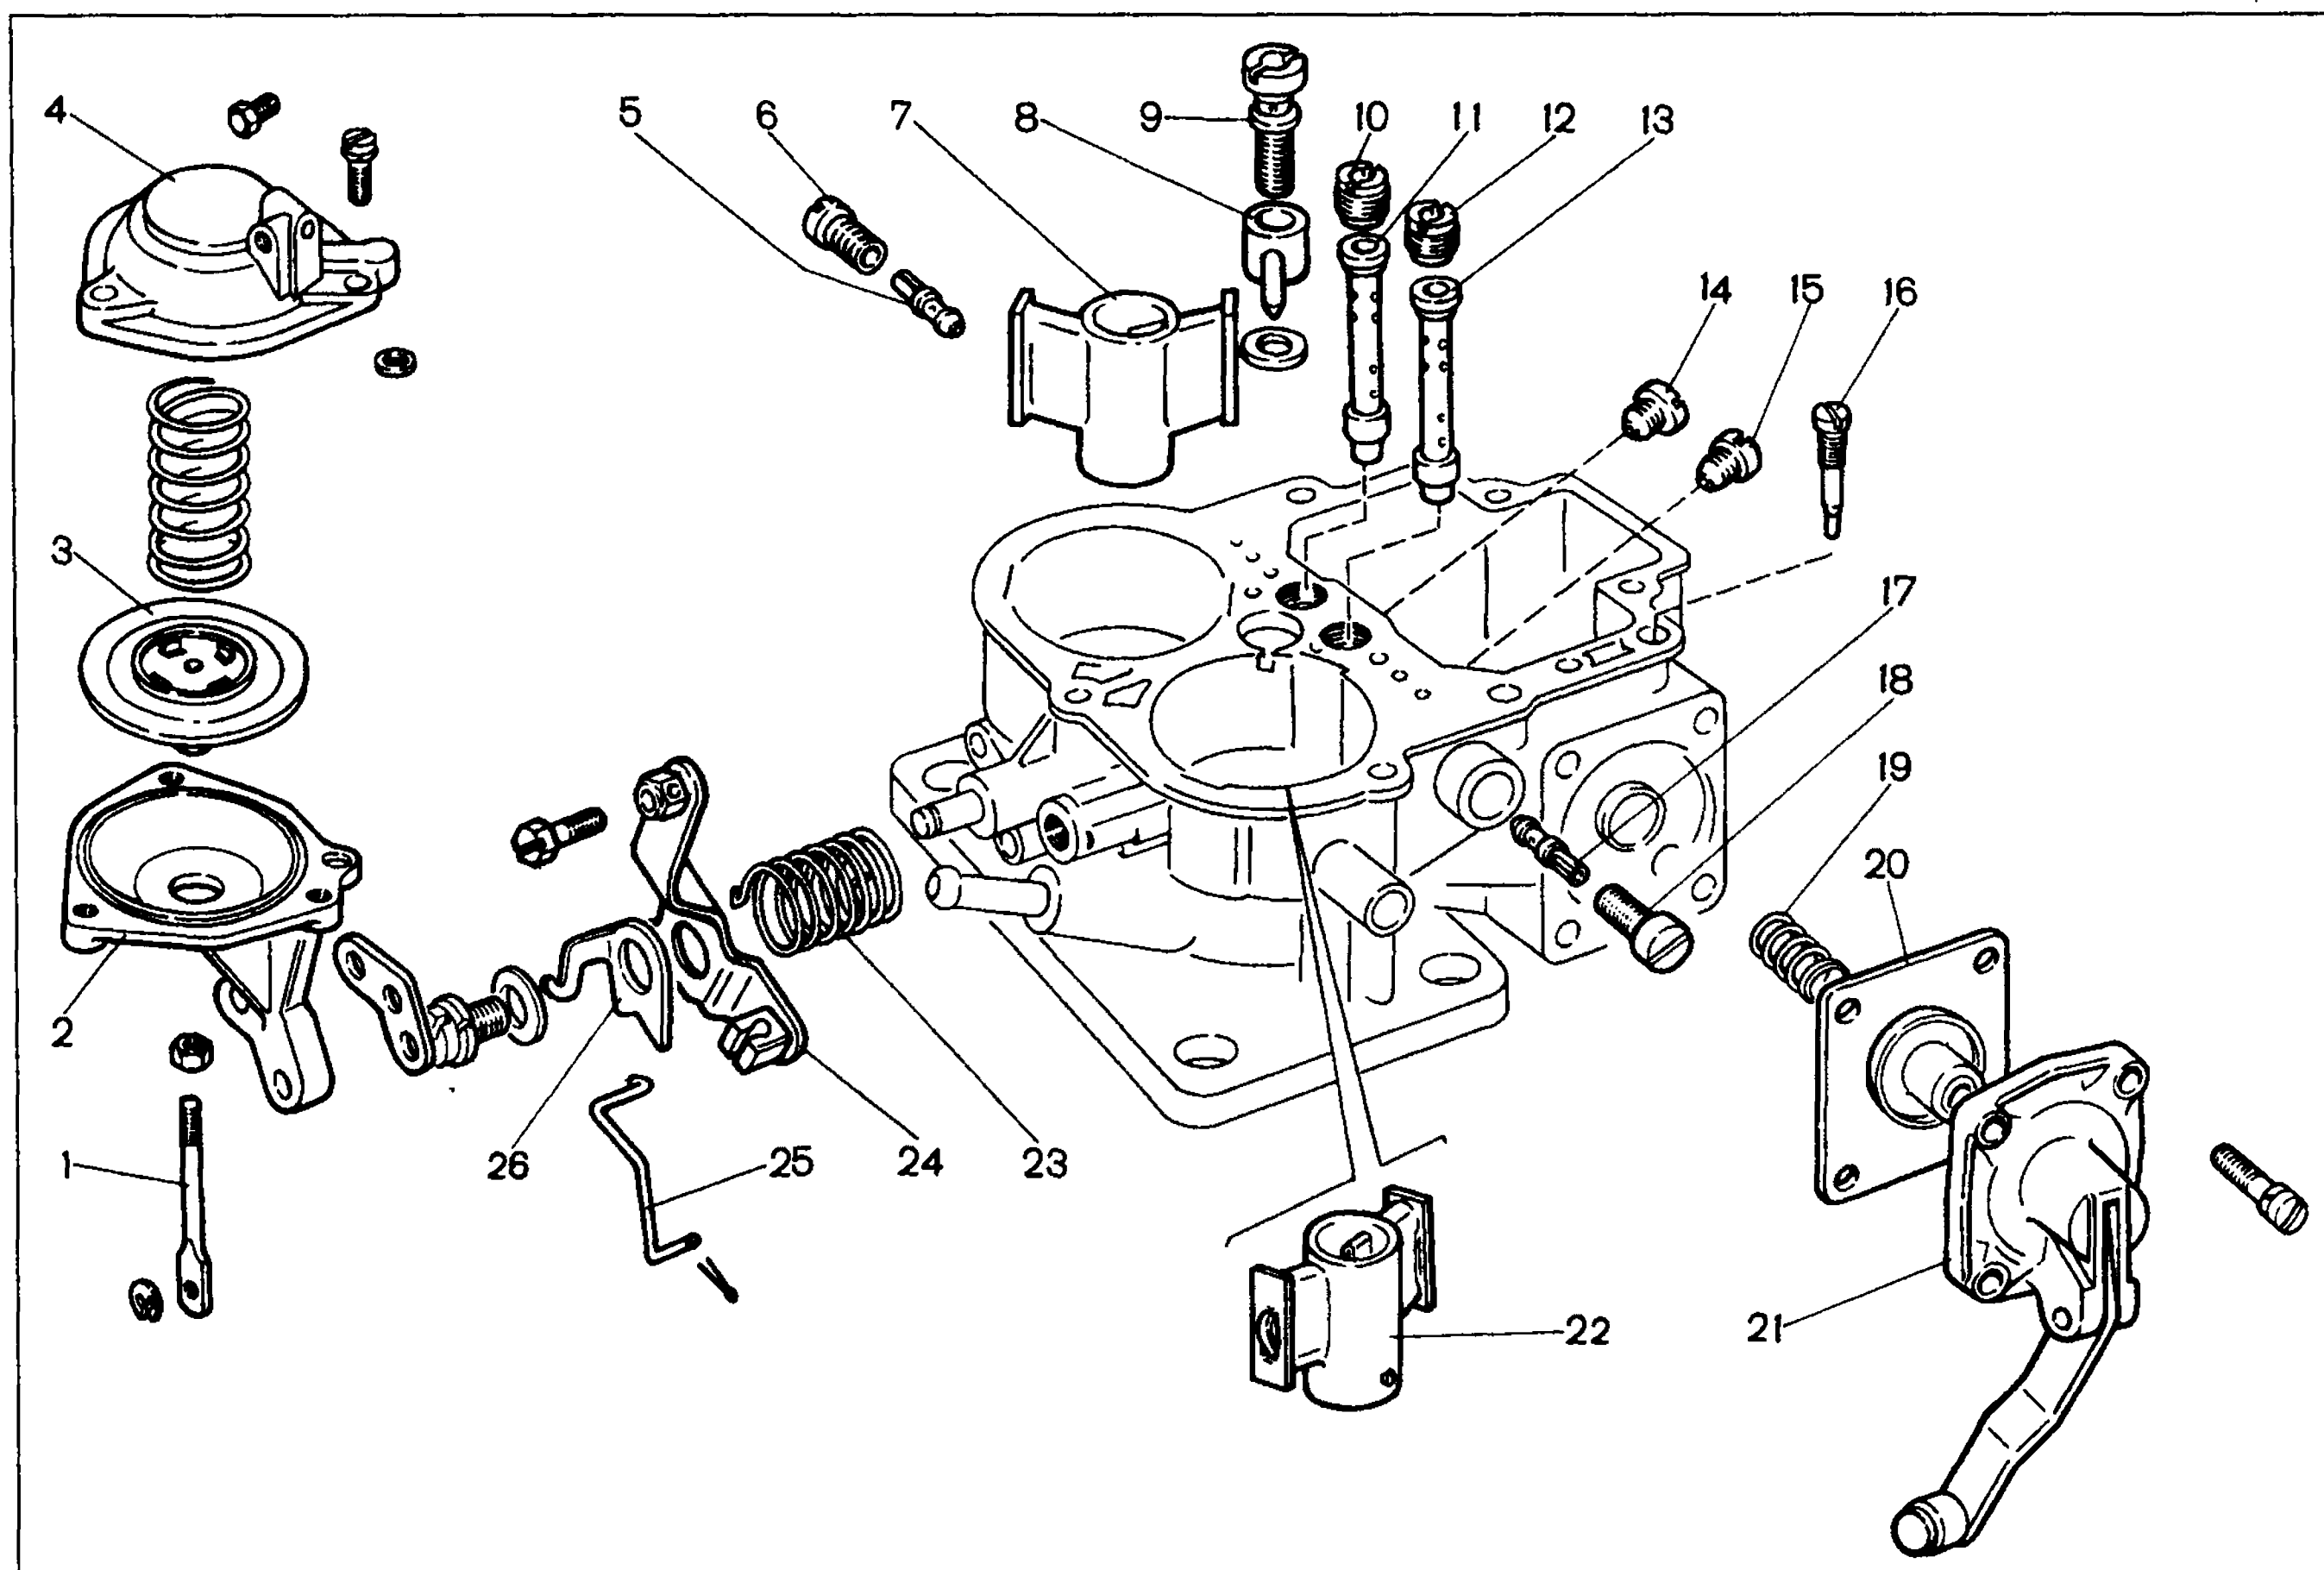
Детали корпуса карбюратора 2107-1107010:
